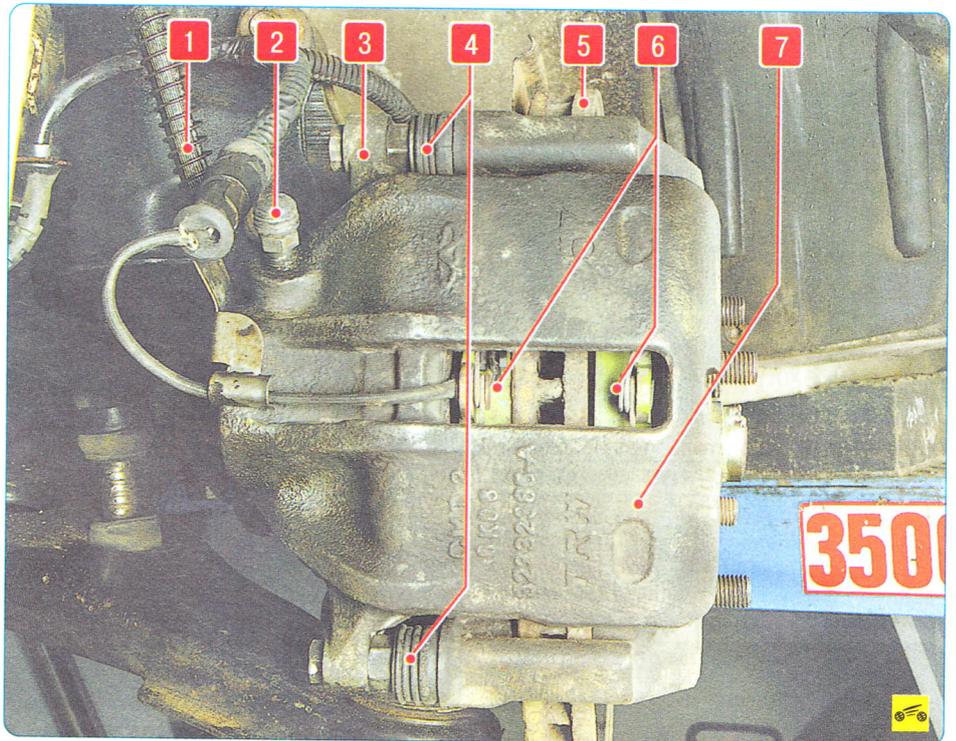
Тормозной механизм переднего колеса: 1 – тормозной шланг; 2 – клапан выпуска воздуха; 3 – направляющая колодок; 4 – направляющие пальцы суппорта (находятся внутри защитных чехлов); 5 – тормозной диск; 6 – тормозные колодки; 7 – суппорт тормозного механизма
